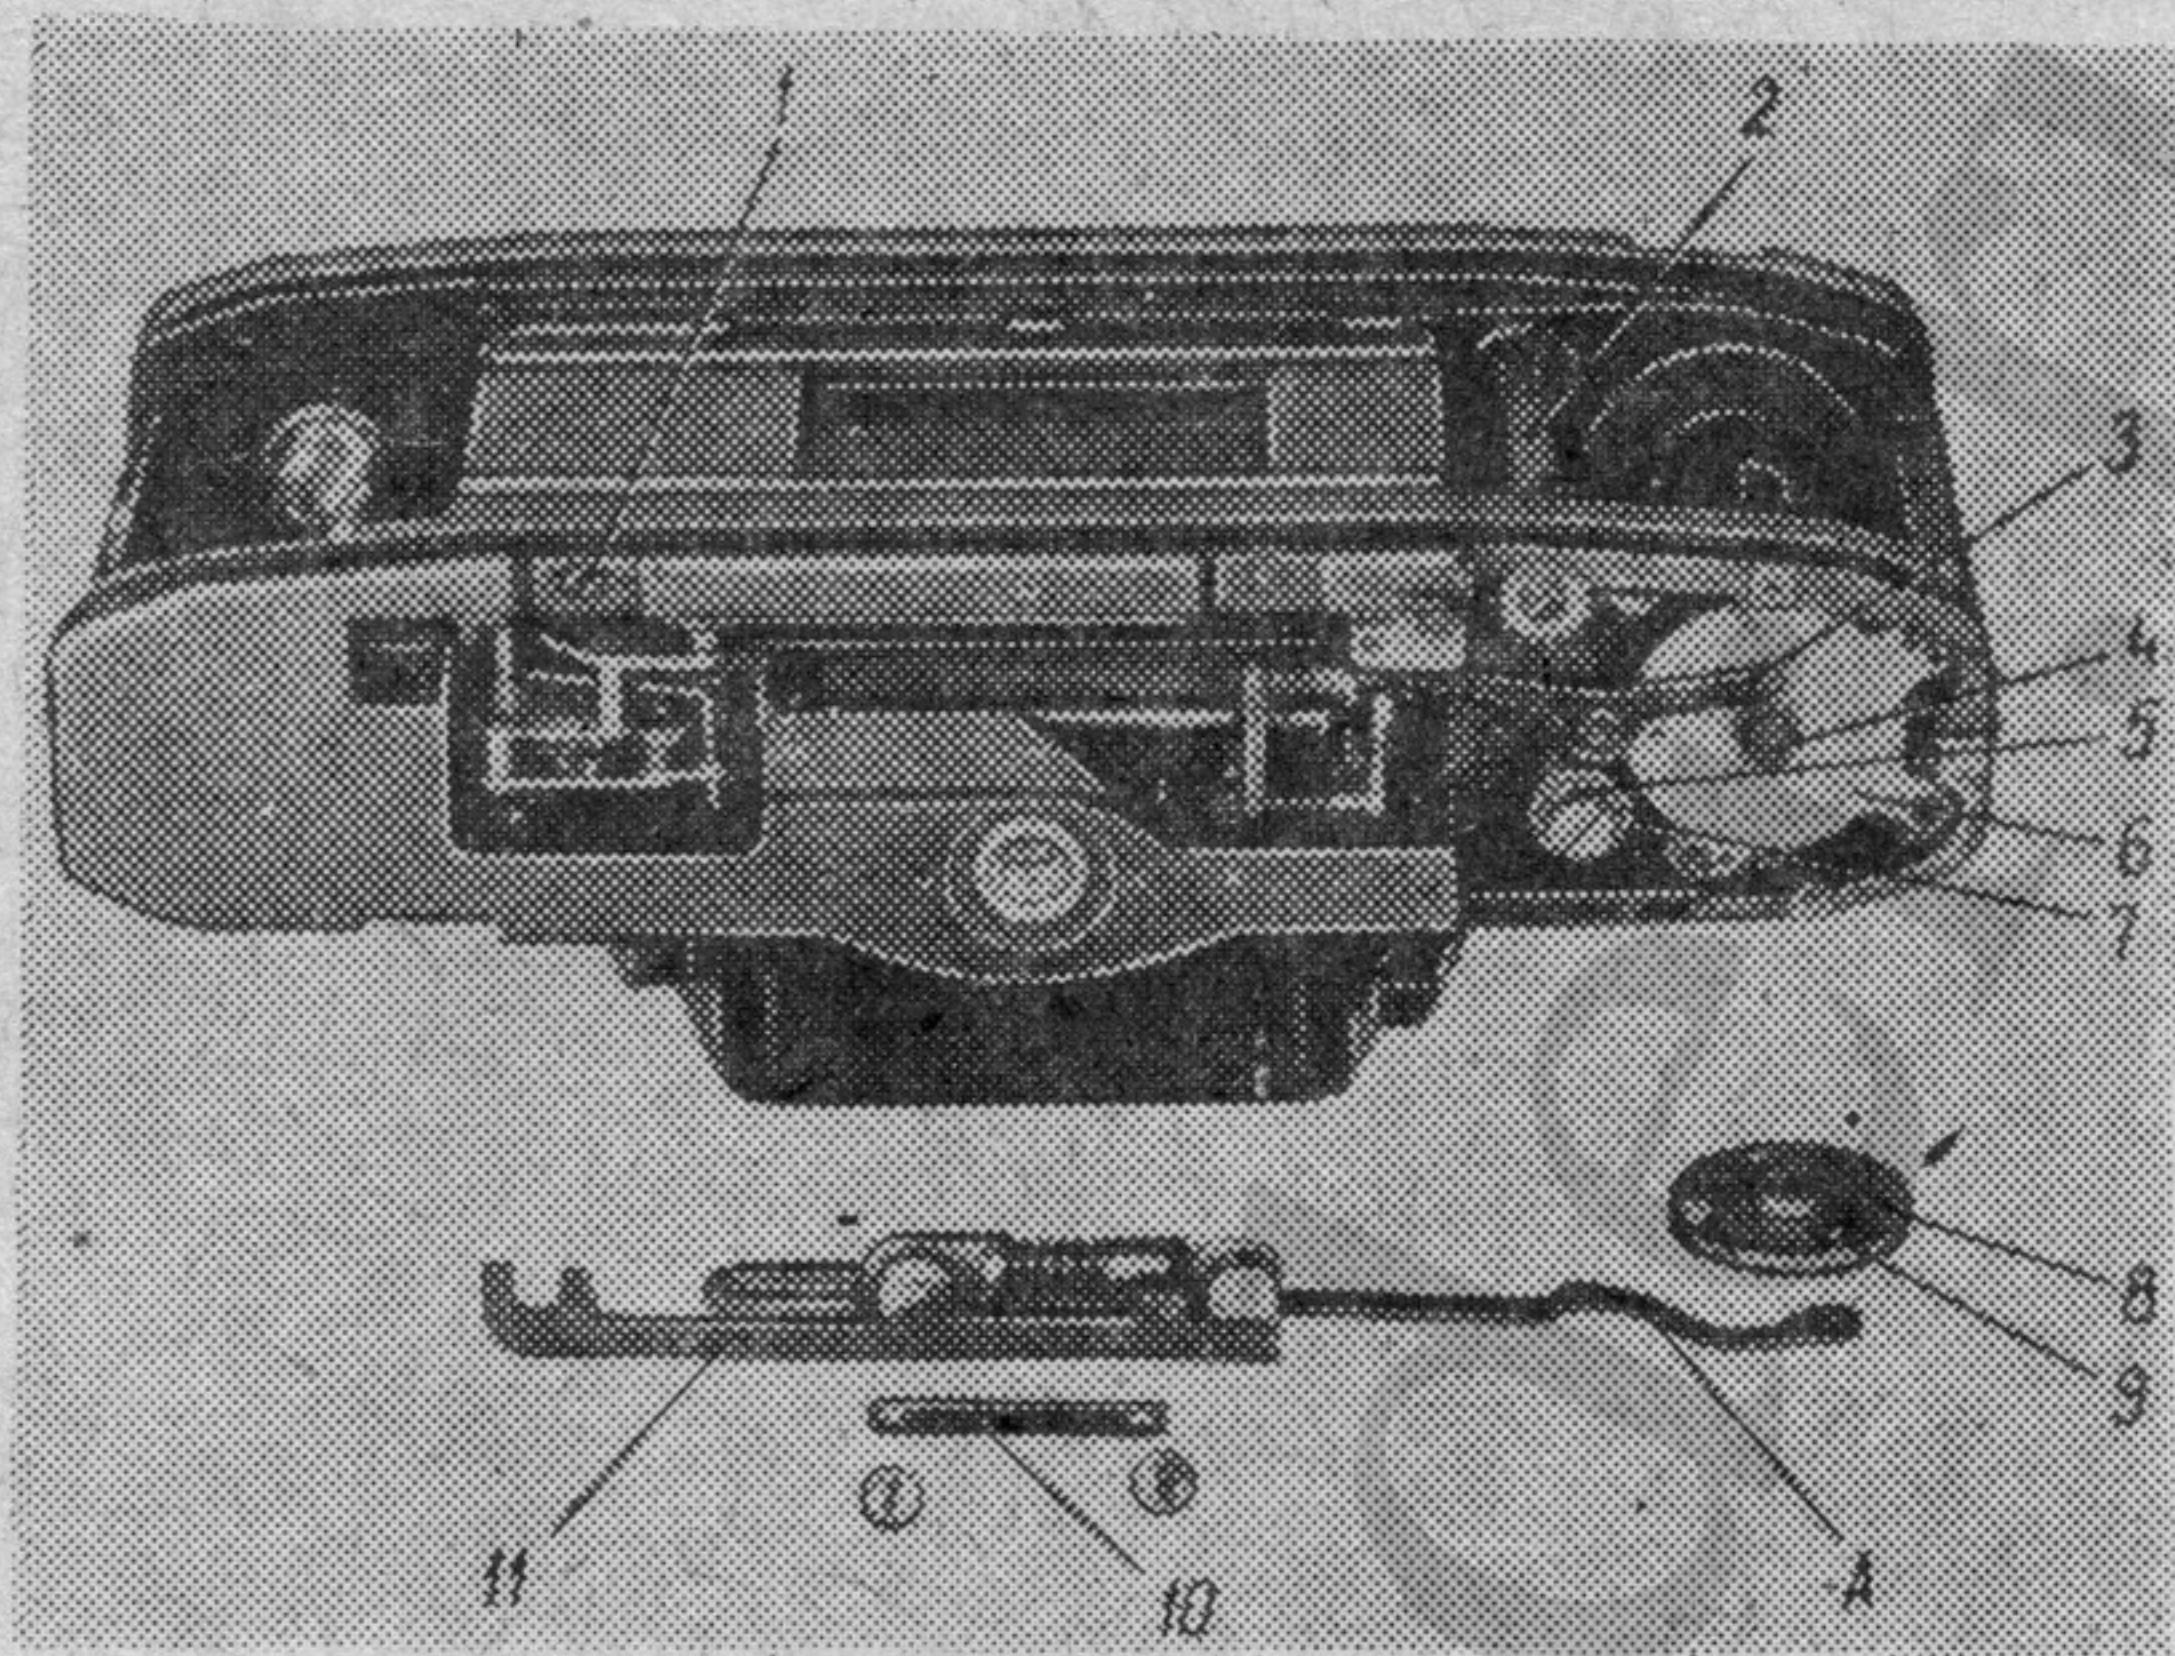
Вид фотоаппарата без нижней крышки со снятым рычагом взвода затвора:
